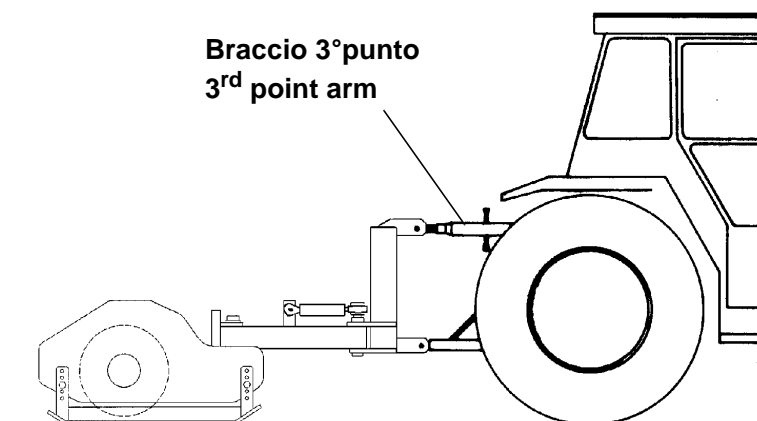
Collegamento alla trattrice - Connection to the tractor
